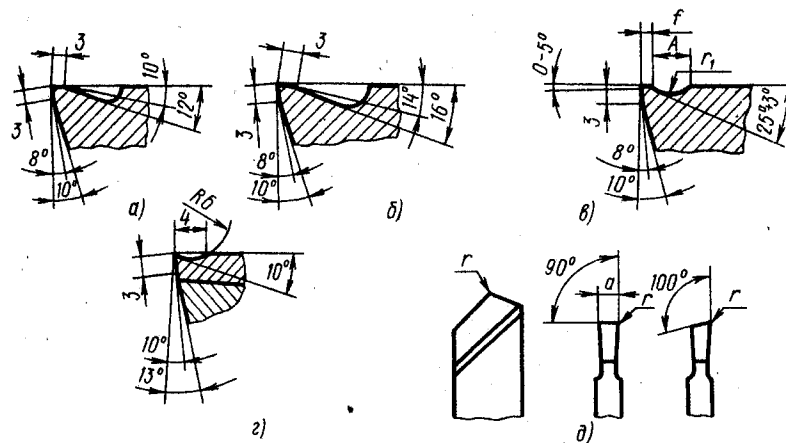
Формы передней поверхности резцов из быстрорежущей стали
